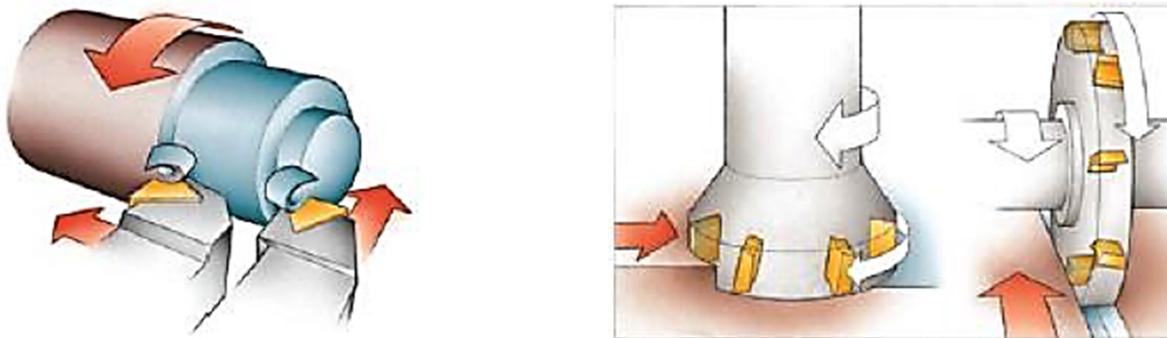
Opérations d'usinage à l'outil coupant : tournage et fraisage.
